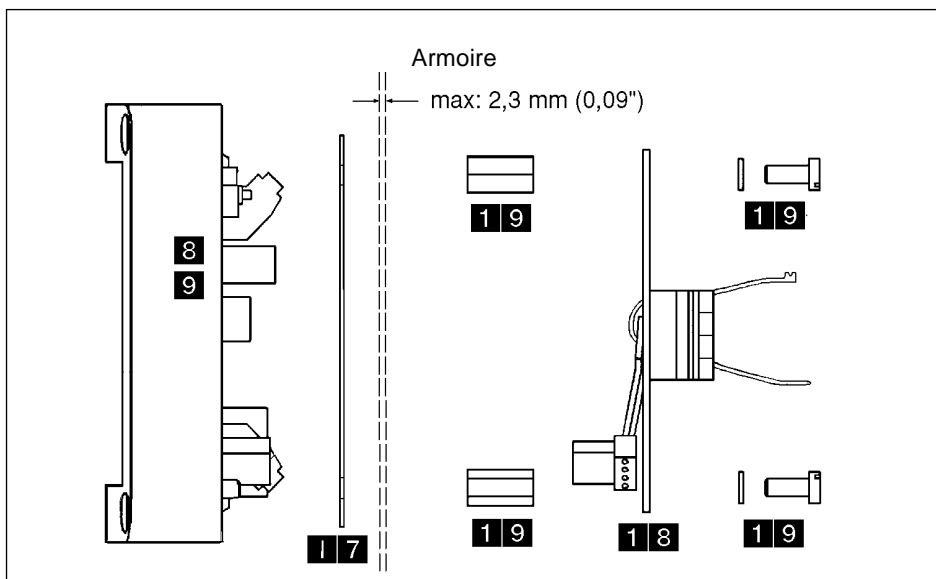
Vue éclatée des pièces de rechange 8025 version encastrable
